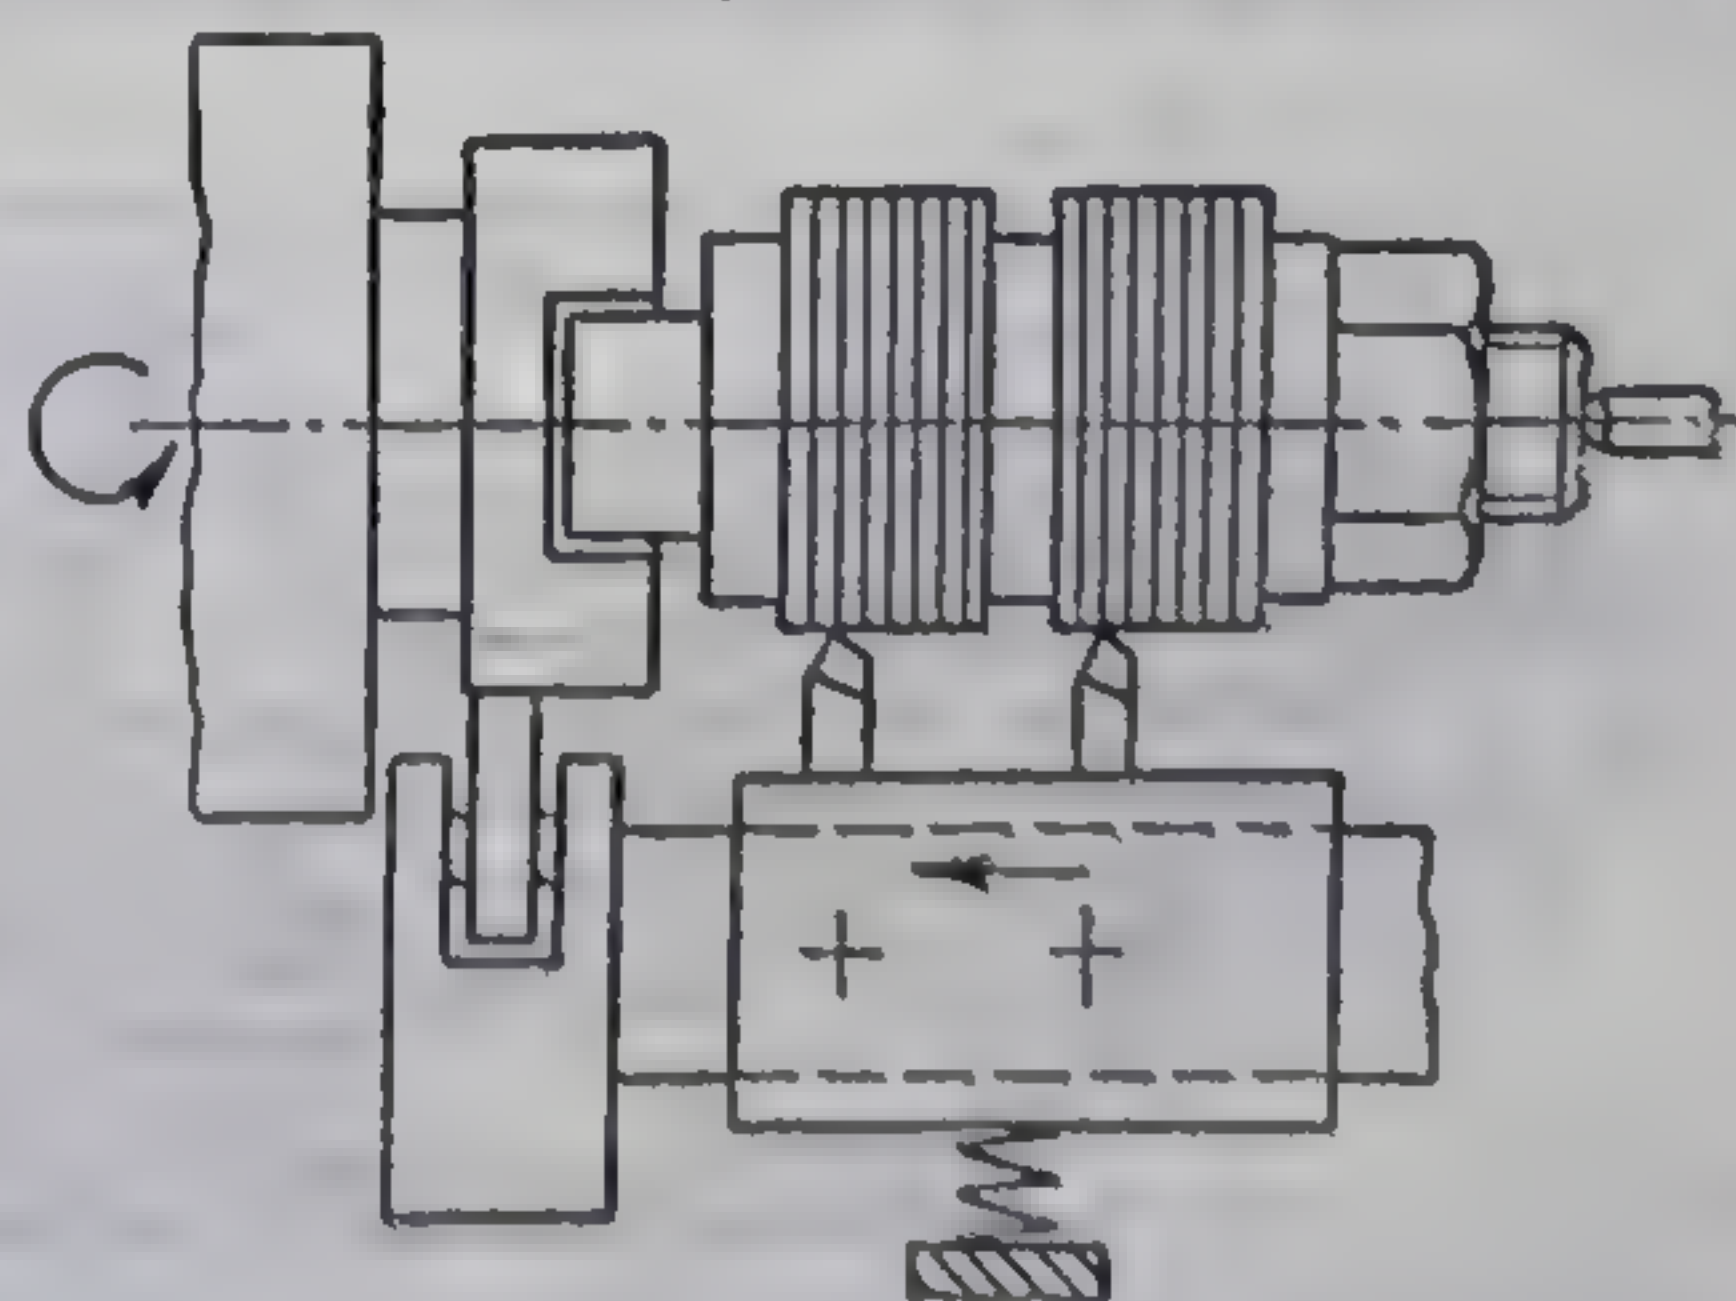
Strunjirea exterioară a segmentelor prin copiere.
